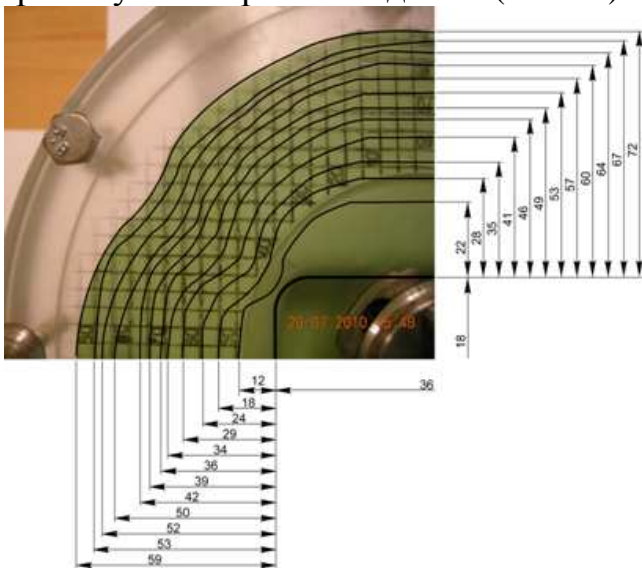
Результати “зворотнього” витягування при різній глибині умовної коробчатої деталі прямокутної форми з розмірами у плані 72x36 мм.
